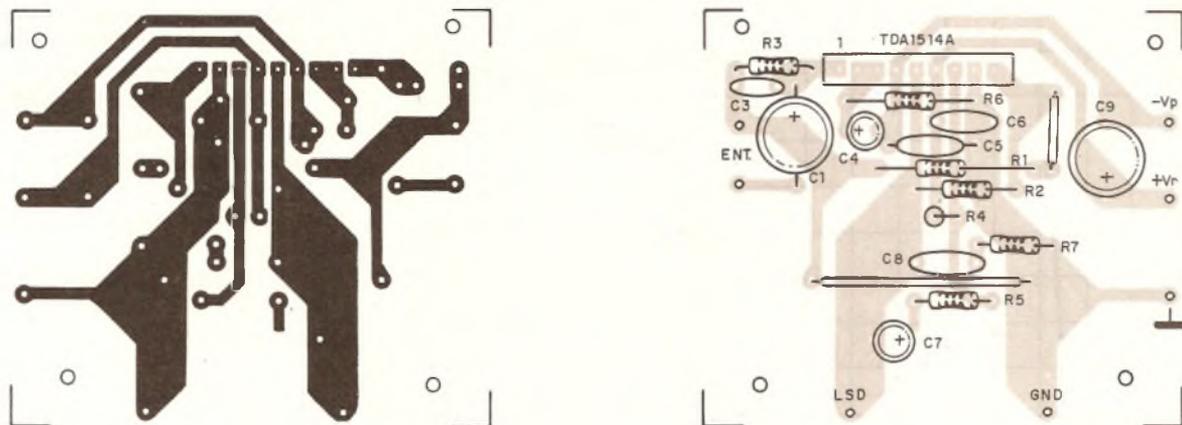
Placa de circuito impresso sugerida pelo fabricante.
